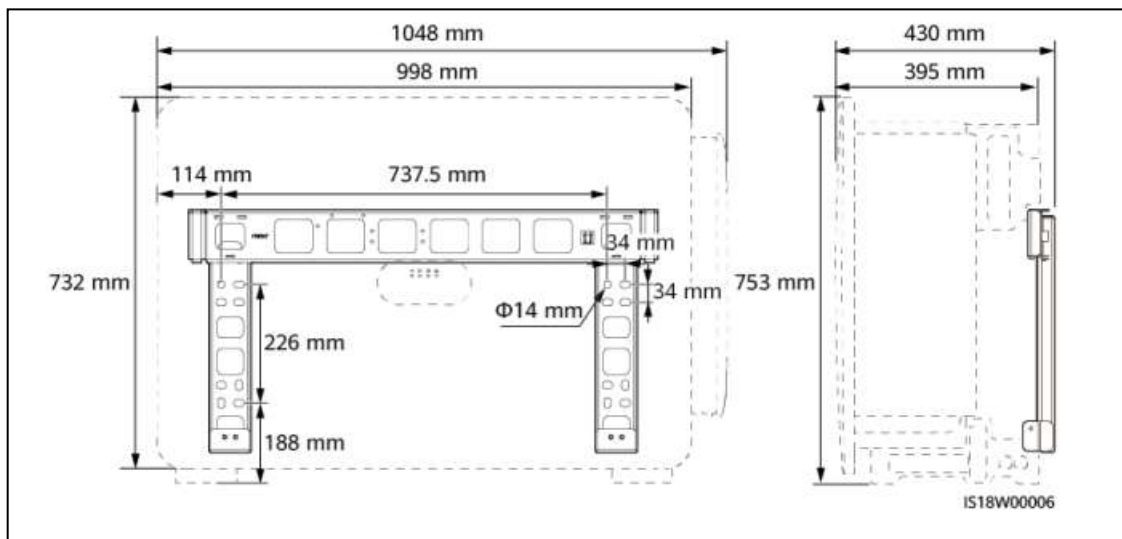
Viste in pianta e in prospettiva dell'inverter SUN2000-330KTL-H1.
